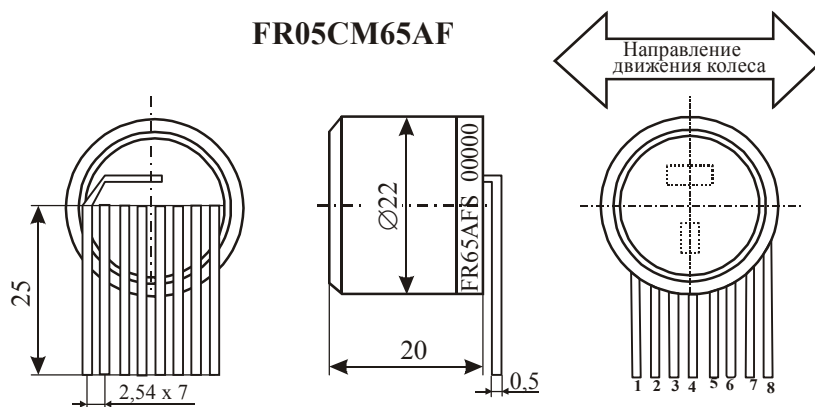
Внешний вид и габаритные размеры датчиков типа FR05CM65AF
